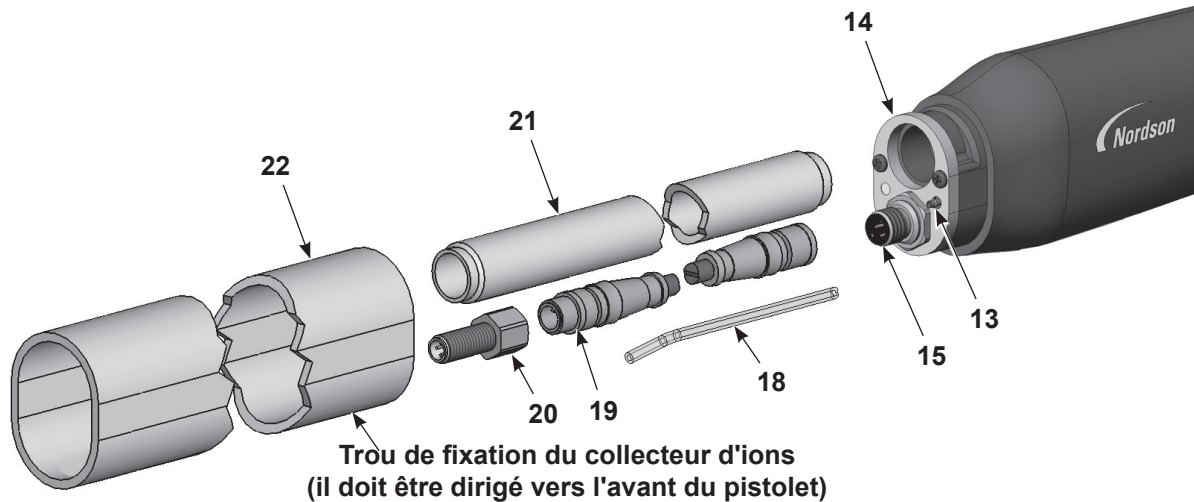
Démontage du pistolet à fixation sur tube 2 sur 5
